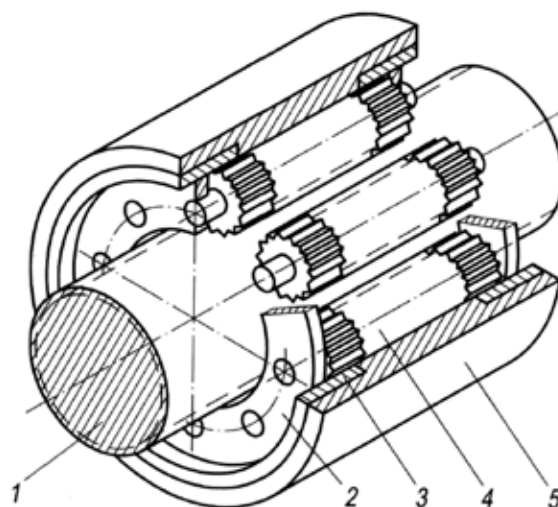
Планетарный роликовинтовой механизм. 1 – винт; 2 – сепаратор; 3 – втулки 4 – ролики; 5 – гайка
